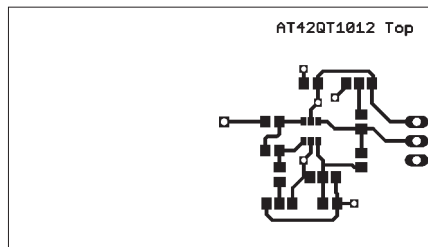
Layoutentwurf für die Bestückungsseite der AT42QT1012-Platine
